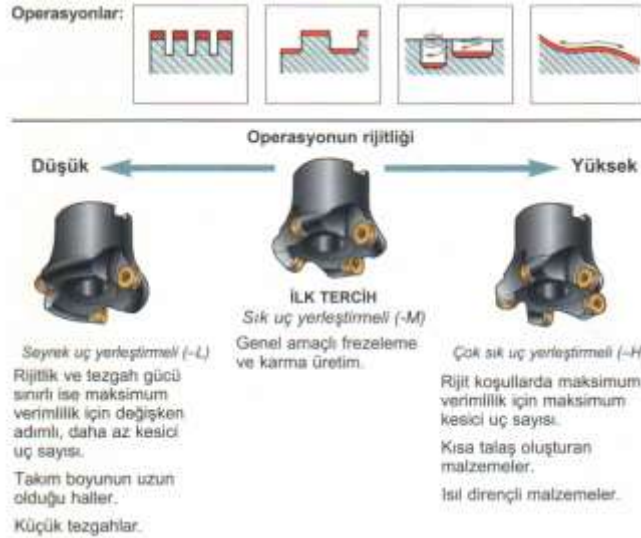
a Parmak frezeleme işlemleri için kesici takım örnekleri
